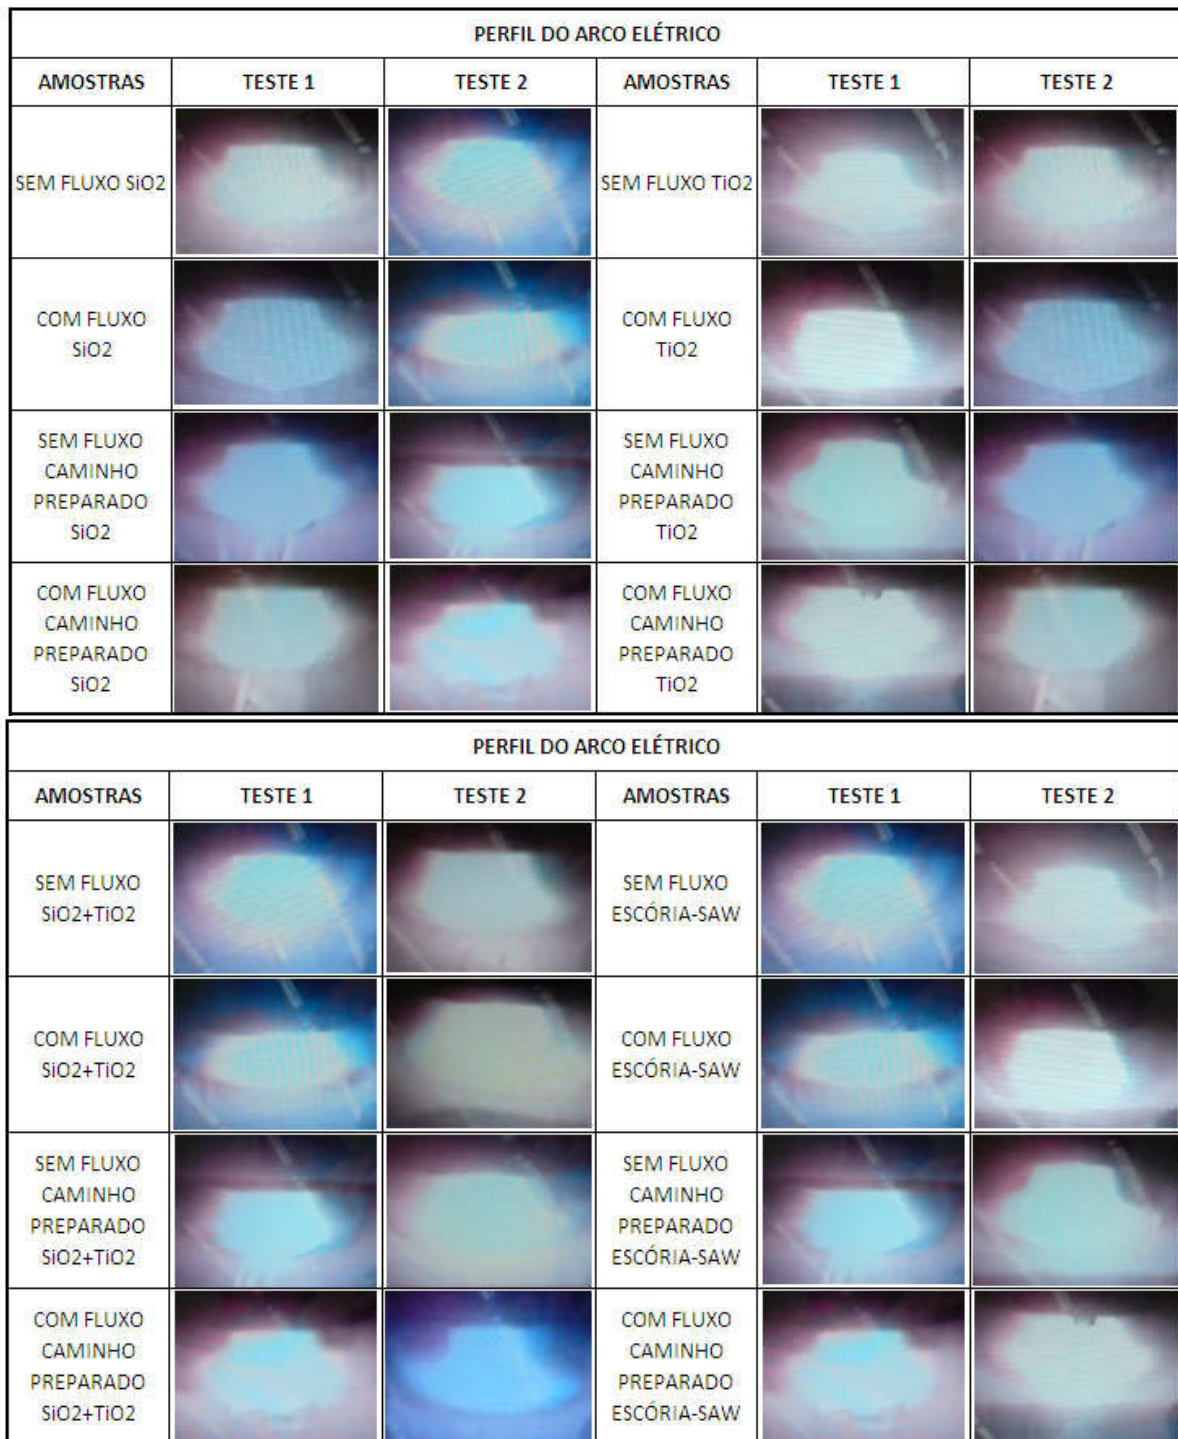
Imagens do arco elétrico durante o processo de soldagem a arco plasma.
